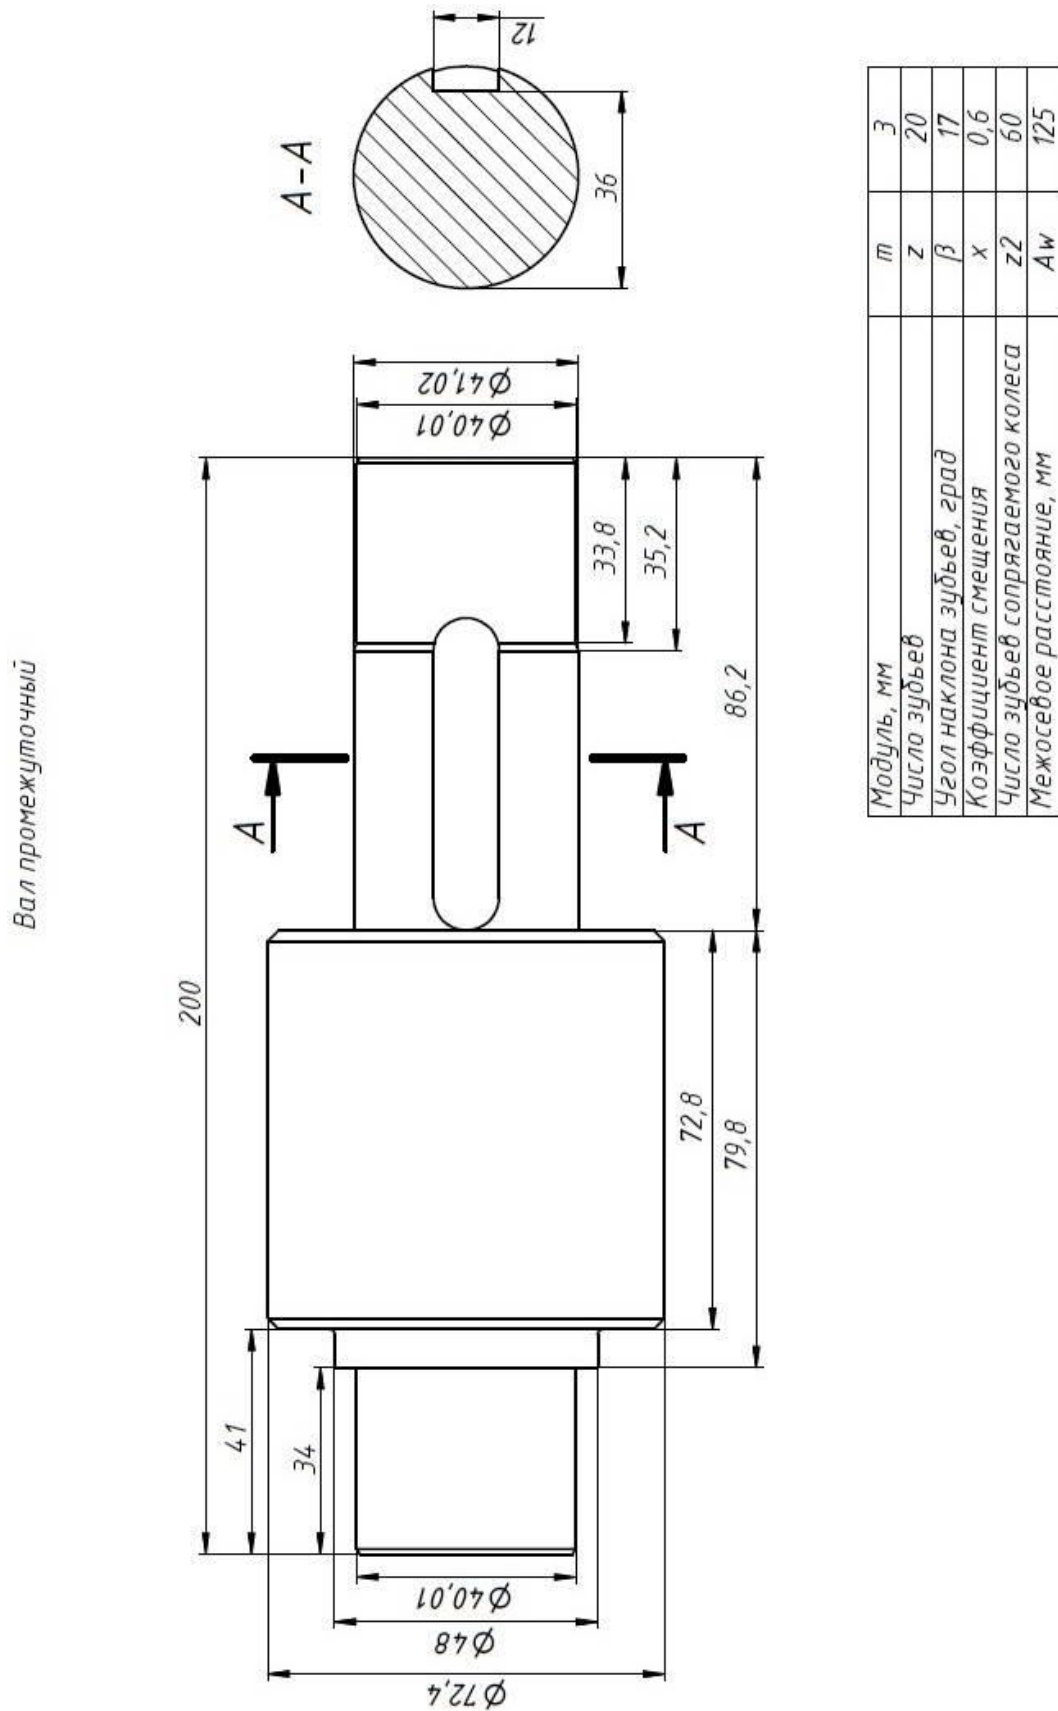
Чертеж вала-шестерни редуктора с эвольвентным зубчатым зацеплением
